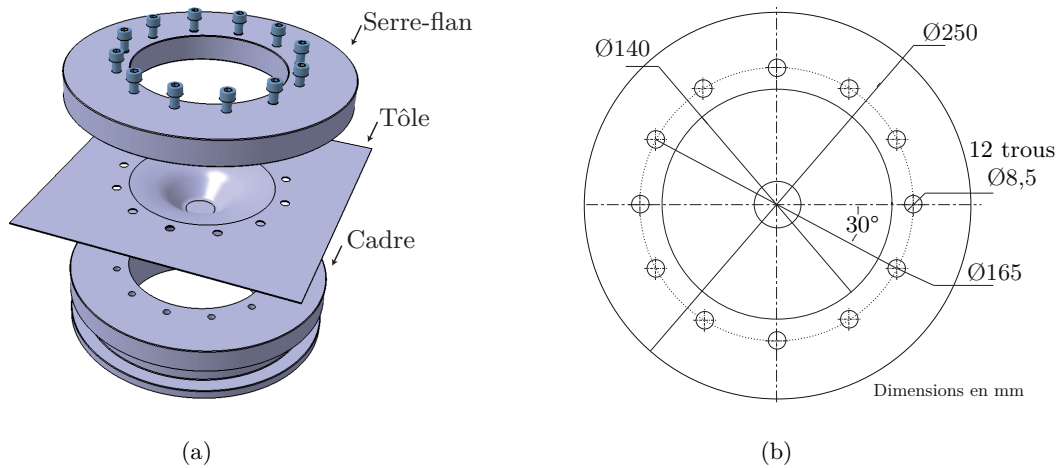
Système de serrage (a) - vue de dessus du serre-flan (b)
